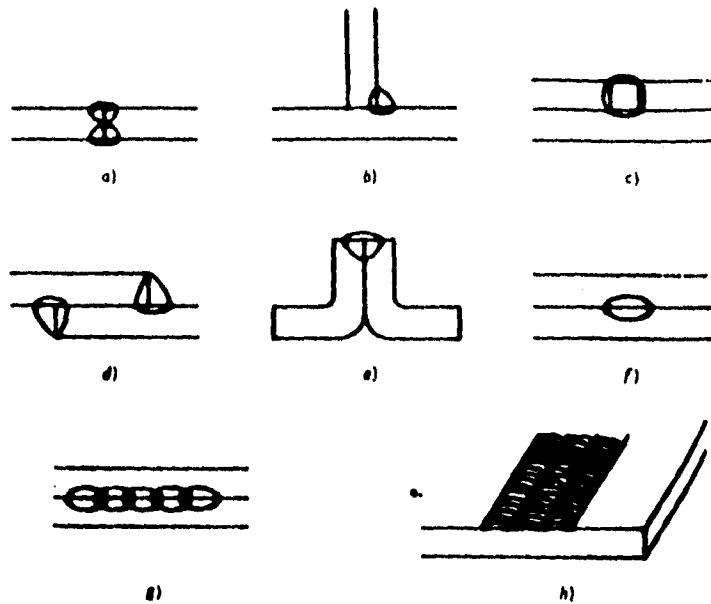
TIPOS DE SOLDADURA: a)SOLDADURA A TOPE; b) SOLDADURA EN ANGULO c) SOLDADURA DE TAPON d) SOLDADURA A SOLAPE e) SOLDADURA AL BORDE f) SOLDADURA POR PUNTOS g) SOLDADURA CONTINUA h) SOLDADURA CON RECARGUE O RECARGUE DURO
